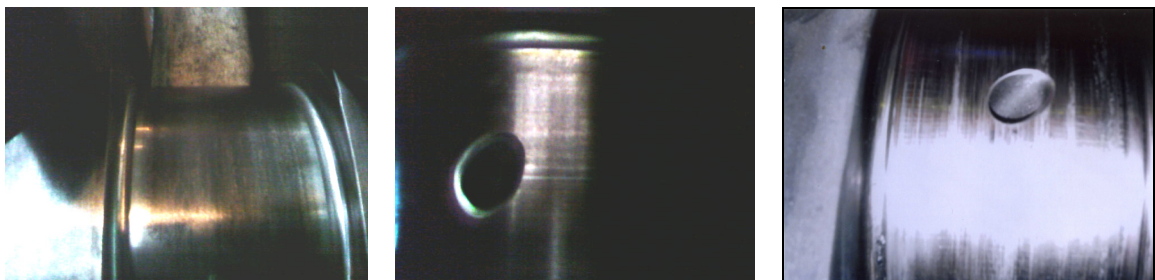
Усталостные трещины на шейке коленчатого вала двигателя типа 5Д49 в условиях ограниченной смазки
